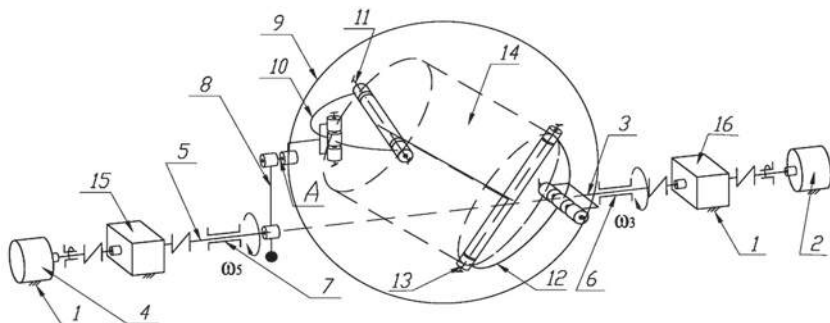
Кінематична схема машини нової конструкції для поверхневої обробки деталей
